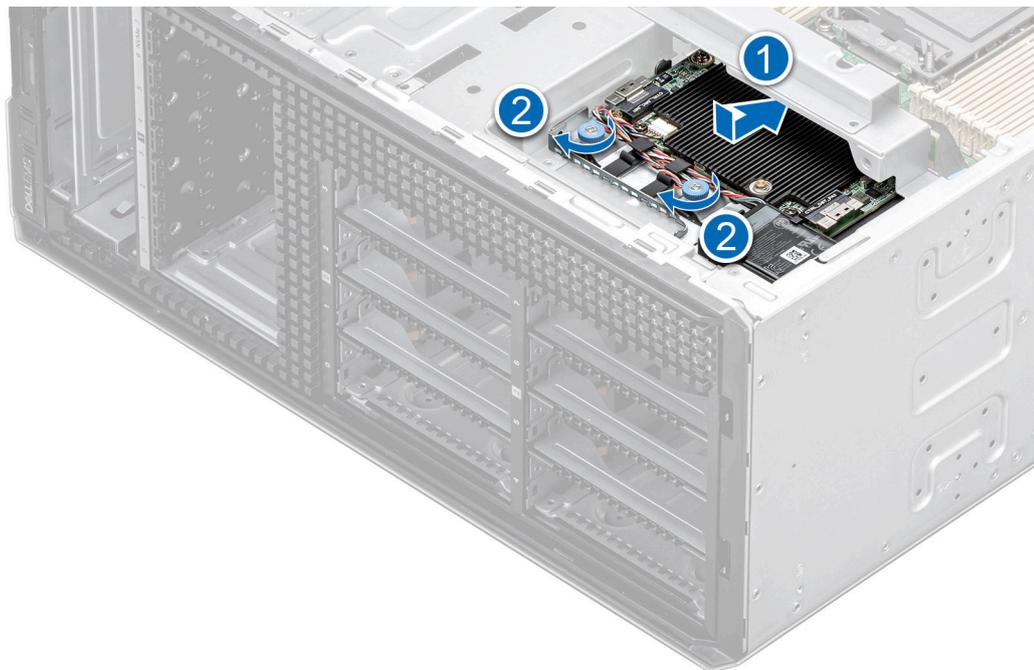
Installation du module PERC avant pour fond de panier de disque de 3,5 pouces.
